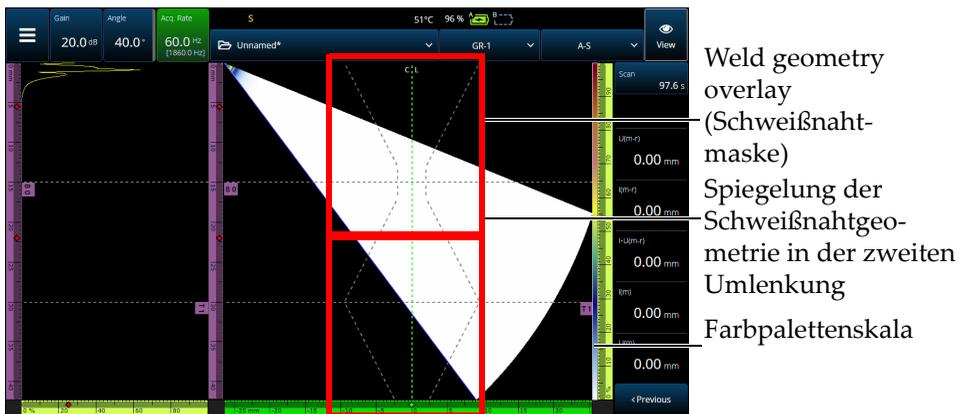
V-Offset weld geometry overlay (Schweißnahtmaske für Tulpe mit Gegenlage)
